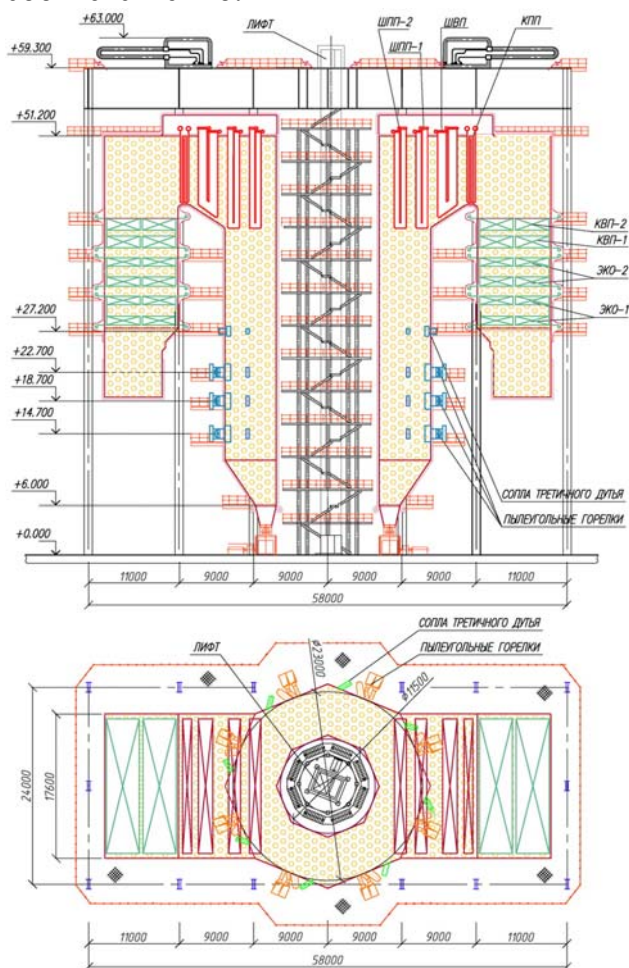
Общий вид котла с кольцевой топкой по типу Пп-1800-27,0-610/610
